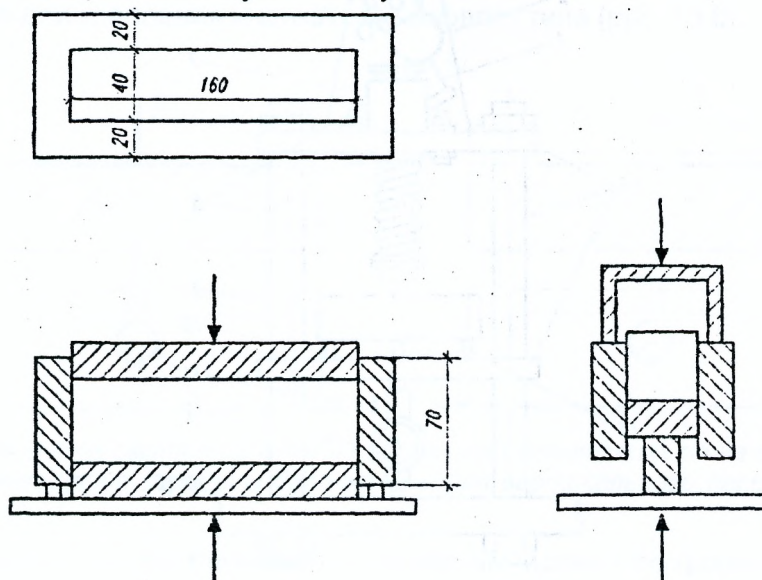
Пресс-форма для изготовления образцов-балочек
